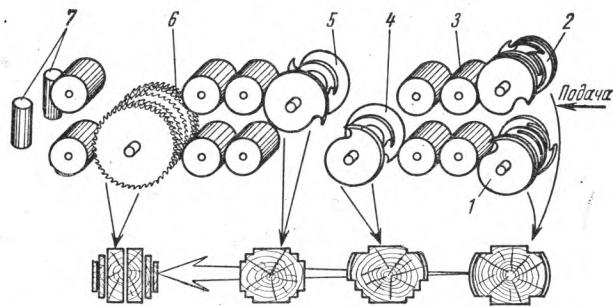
Принципиальная схема работы фрезерно-пильного агрегата ЛАПБ:
